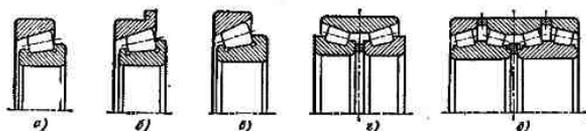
Роликоподшипники конические типов: а — 7000; б — 67000; в — 27000; г — 97000; д — 77000
